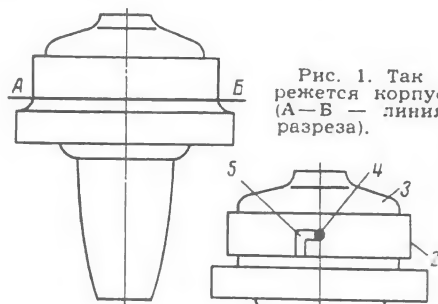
Отремонтированный датчик: 1 — корпус; 2 — кольцо; 3 — крышка; 4 — штифт; 5 — фигурный паз.
